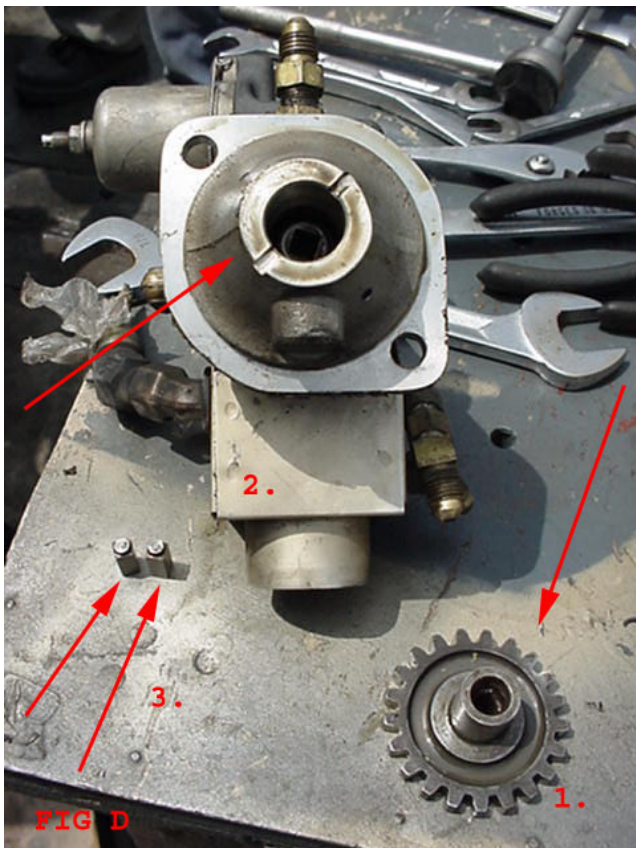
Engranaje de la bomba, 2. Bomba de combustible, 3. Coupling roto.
